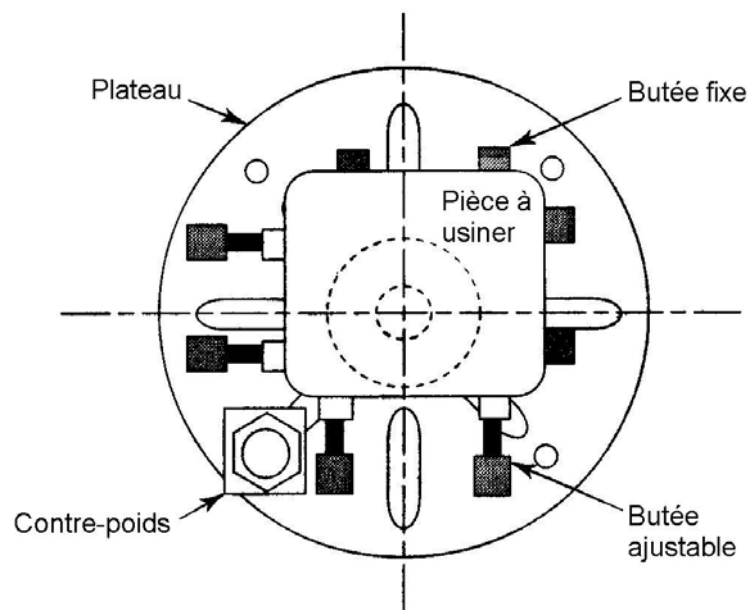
Sur un plateau plat (pousse toc) de tour.
